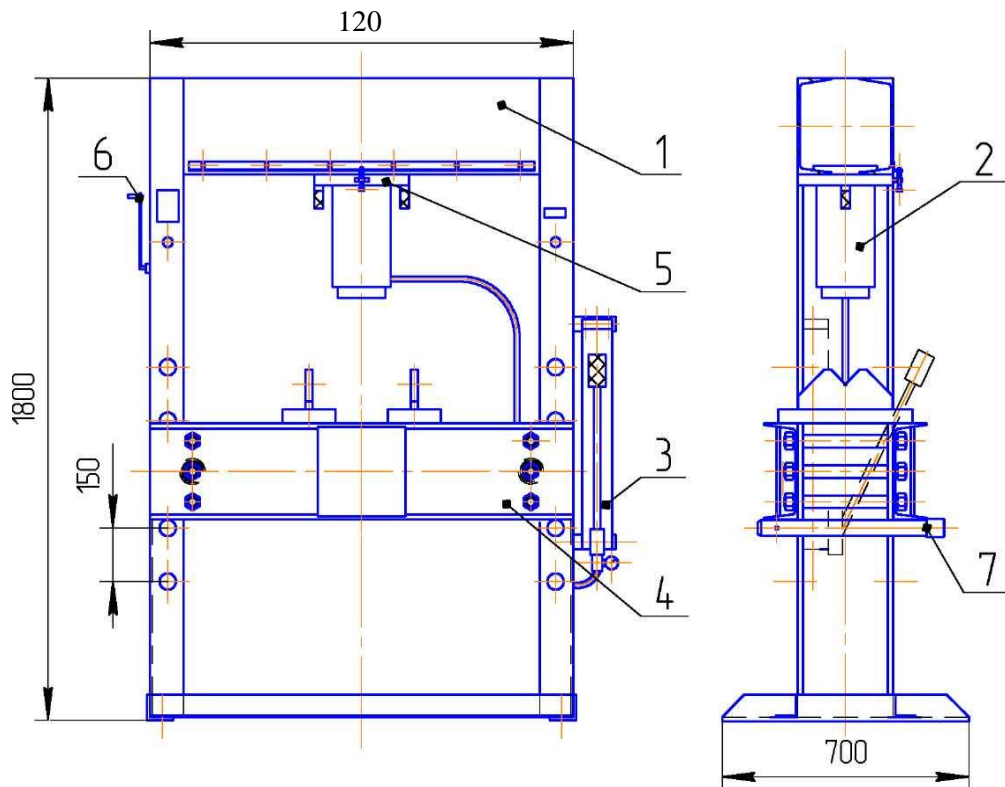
Пресс гидравлический ПГП-30 1- рама; 2- цилиндр гидравлический; 3- насос гидравлический; 4- стол передвижной; 5- каретка подвижная; 6- рукоятка лебёдки; 7- палец
